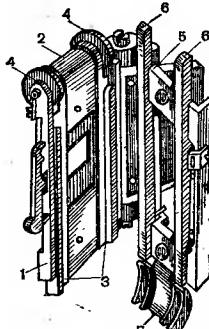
Общий вид фильмо-вого канала кинопроектора типа КН: 1 — основание канала; 2 — вкладыш; 3 — рабочие поверхности; 4 — поперечно-направляющий ролик; 5 — дверца; 6 — прижимные полозки; 7 — полукруглый прижимной полозок
